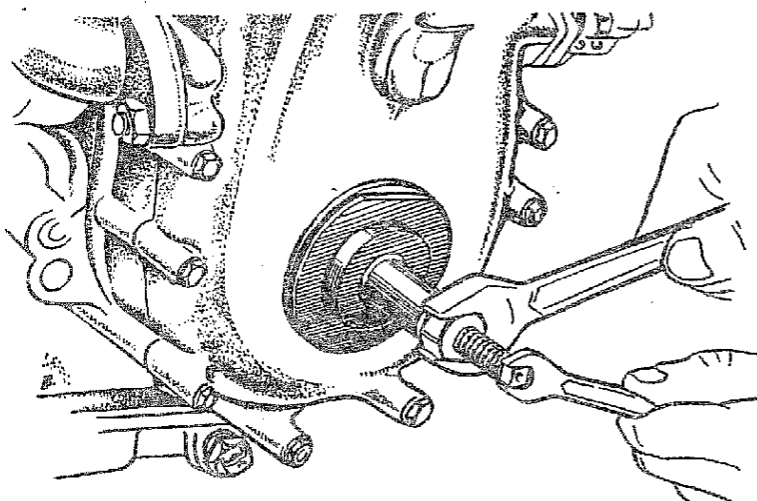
Запрессовка сальника коленчатого вала в крышку распределительных шестерен
